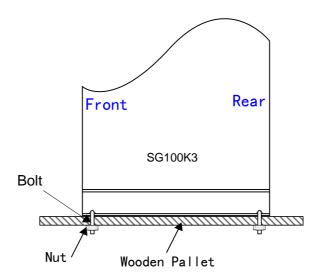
Vista trasversale del dispositivo SG100K3 fissato sul pallet di legno
